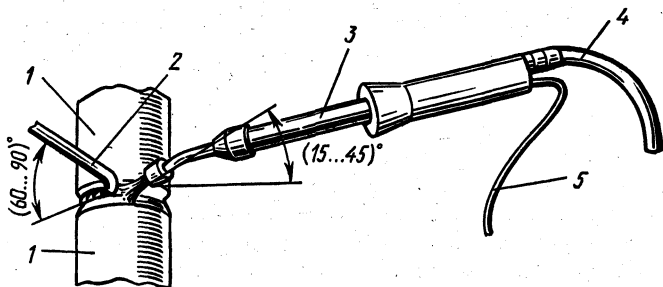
Сварка пластмассовых труб нагретым газом с применением присадочного материала:
